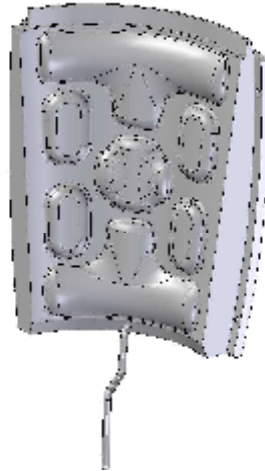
Moldes para la bolsa sujetadora lateral
